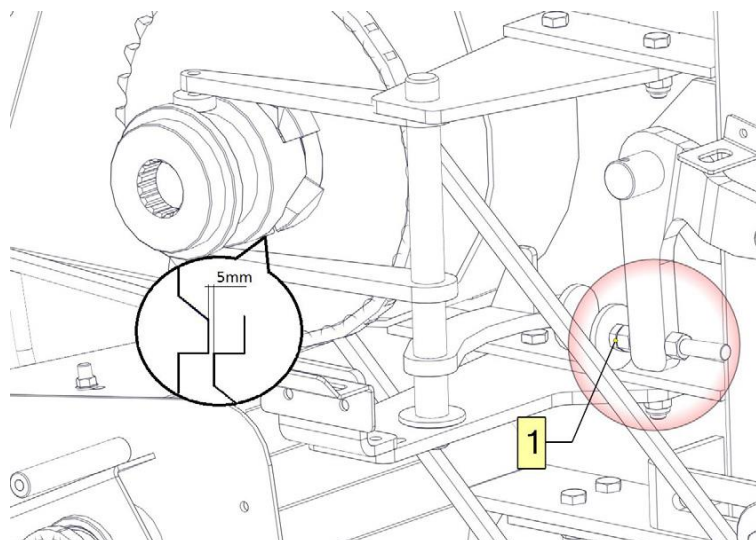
Регулировка натяжения цепно-пруткового транспортера пресс-подборщика Z587/1
